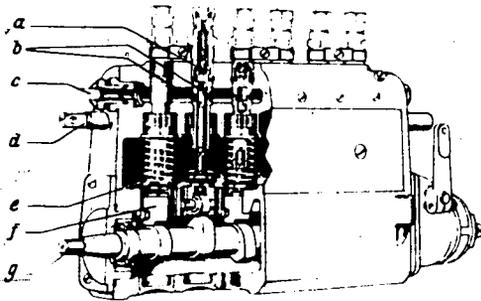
a 6-Zylinder-Bosch-Einspritzpumpe
